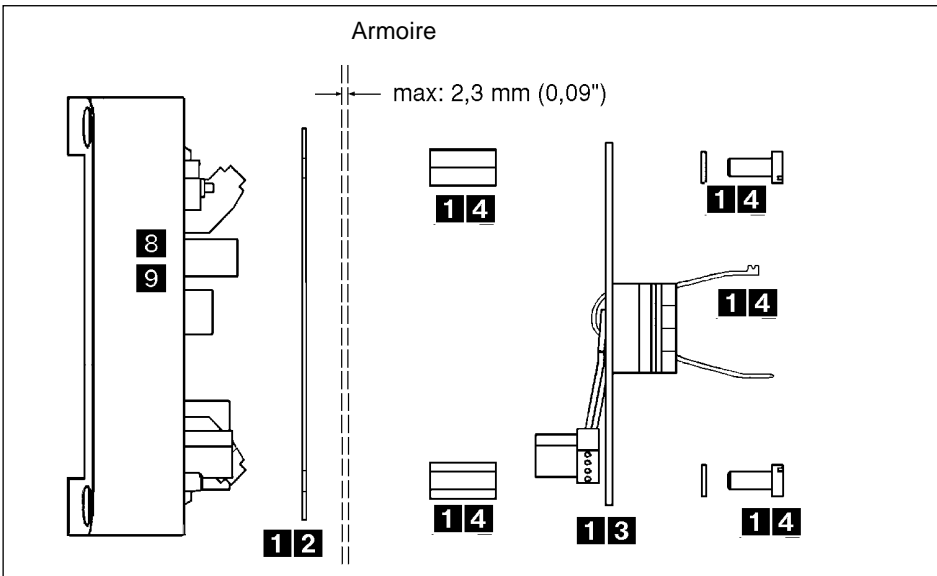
Vue éclatée des pièces de rechange 8025 version encastrable
